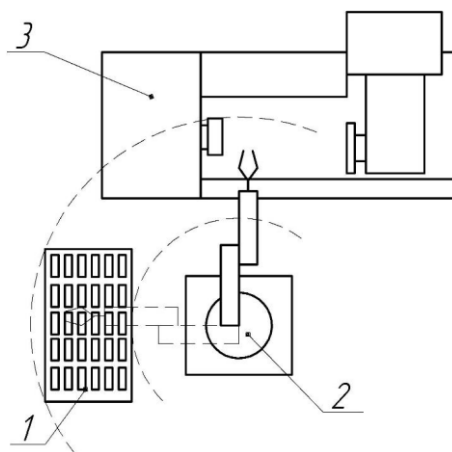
Схема автоматизированной ячейки токарного станка с ЧПУ
